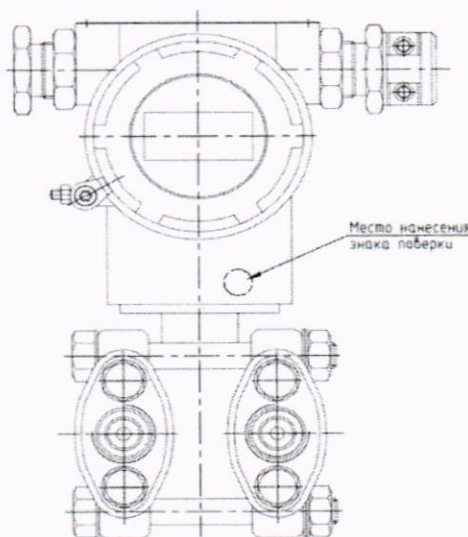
Место нанесения знака поверки на корпус датчика
